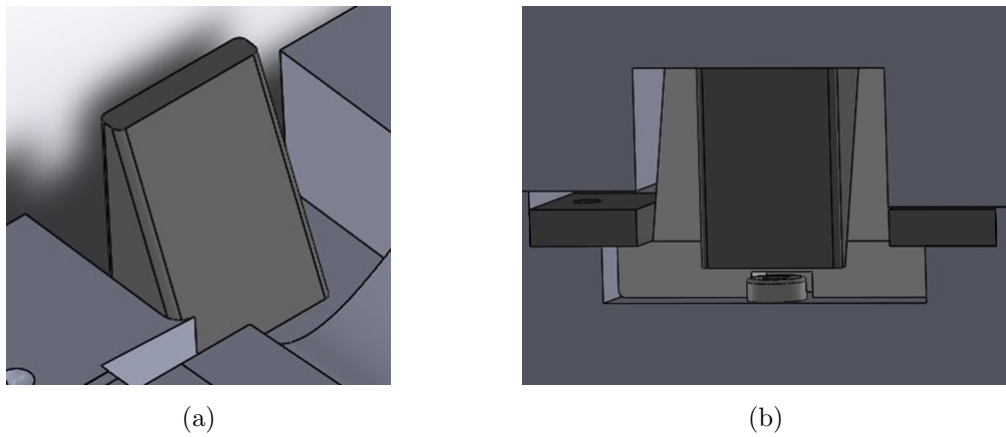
Cunha para fixação do macho, a) aspecto do cunha, b) molde fechado com cunha a fixar o macho
